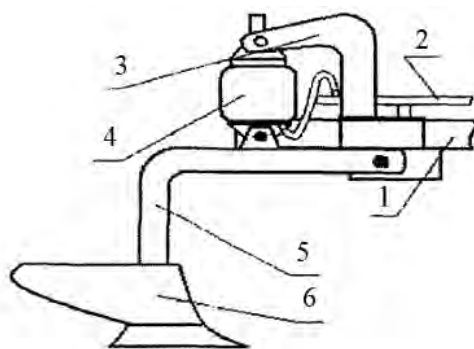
Плужный корпус с пневматическим предохранительным механизмом:
